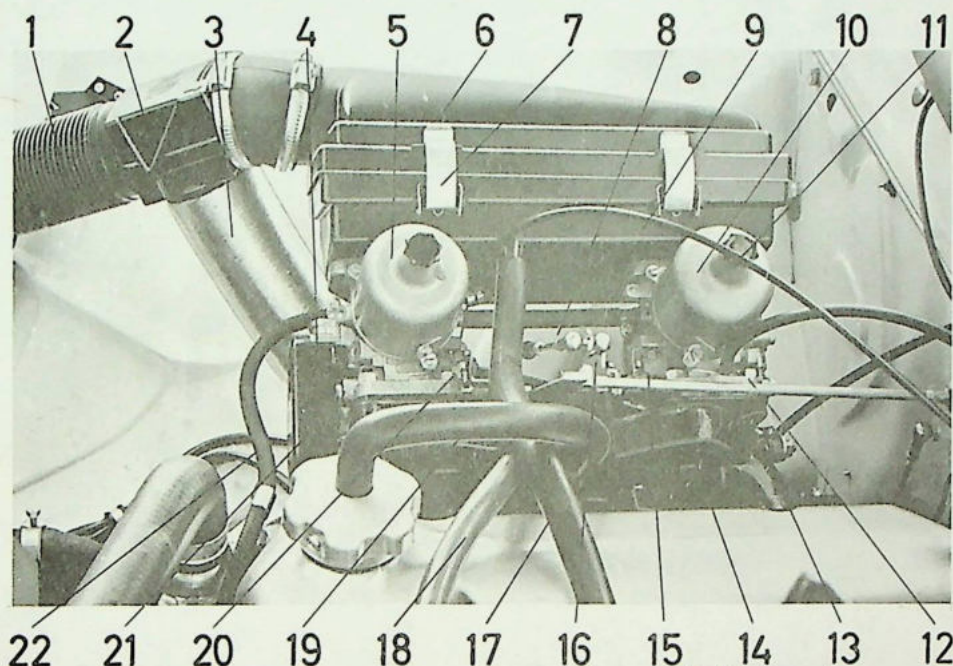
SU-HIF 6 karburateurs gemonteerd op de B 20 B motor.
